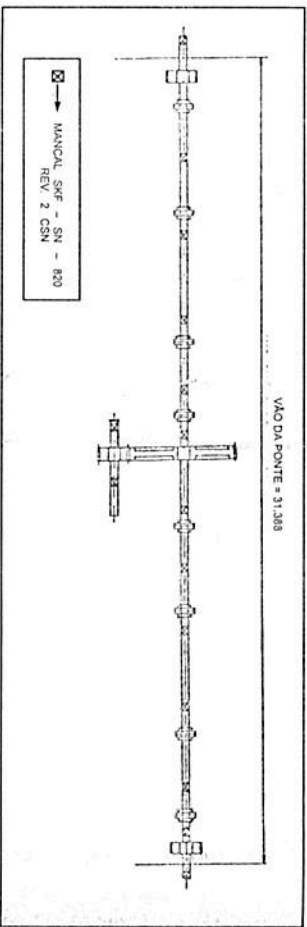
Desenho representativo do eixo principal do conjunto de translação de ponte rolante da CSN.
